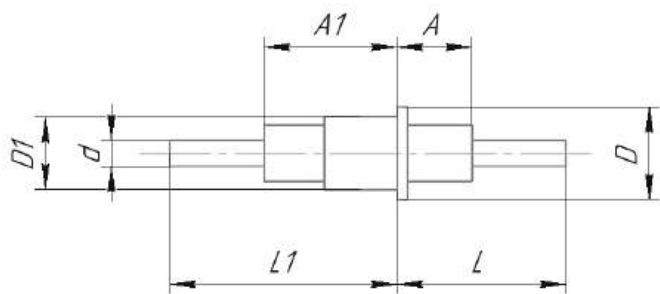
Габаритные размеры фильтров Ф26, типоразмеры 3, 4, 5, 6
